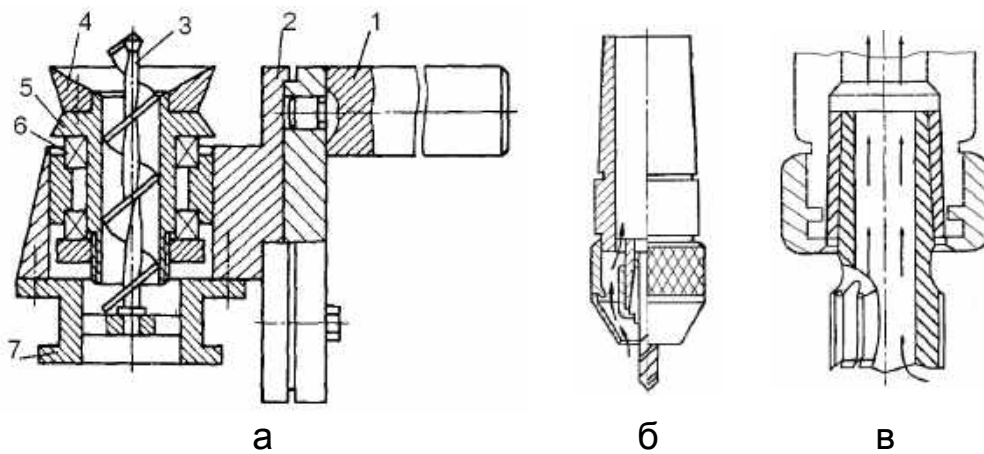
Інструменти спеціальних конструкцій для оброблення деталей із КМ:
